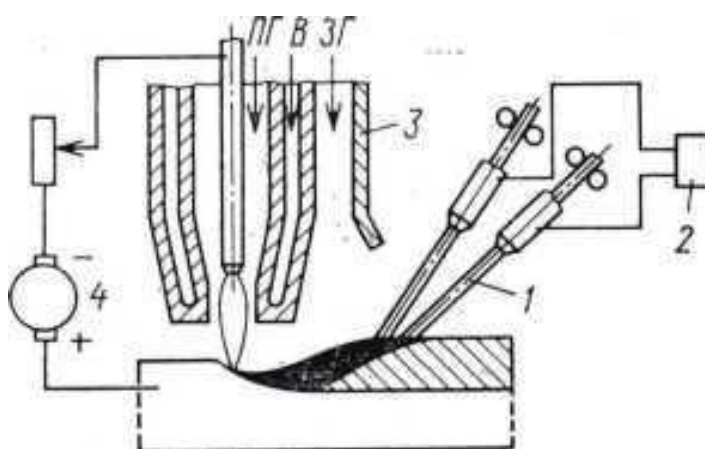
Схема плазменной наплавки с подачей в ванну двух плавящихся проволок:
